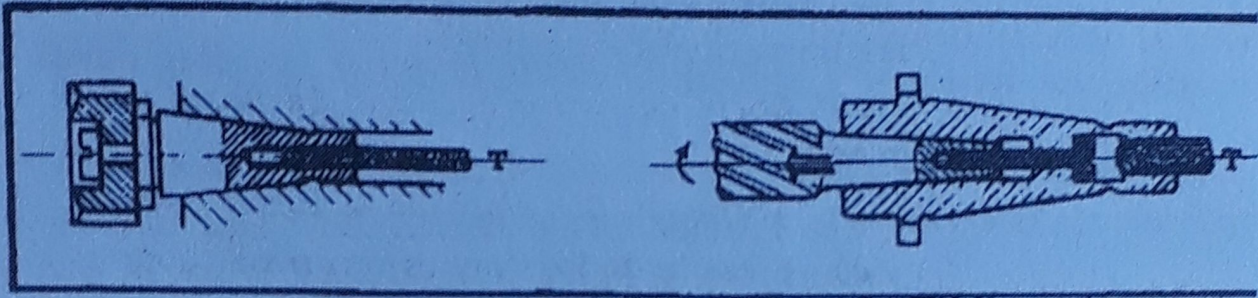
/4. — Montaje de una fresa frontal con agujero: T) Tiran extractor.
